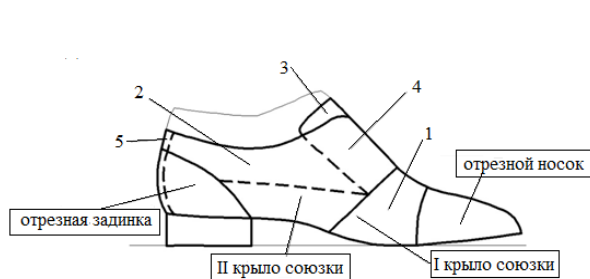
Схема расположения деталей из меха в конструкции полуботинок:
